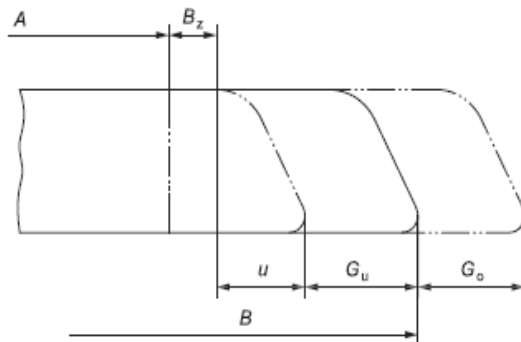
Размеры реза: A – сборочный размер; B – номинальный размер стороны реза; B_z – припуск на механическую обработку; G_o – верхнее предельное отклонение; G_u – нижнее предельное отклонение; u – допуск перпендикулярности
